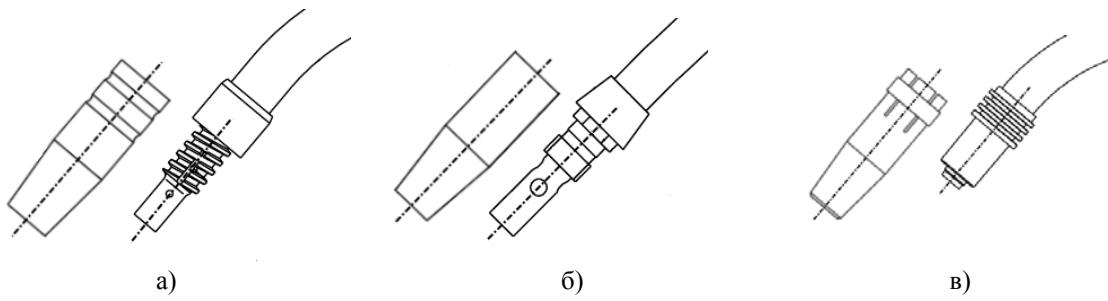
Конструкции крепления сопел к сварочным горелкам
